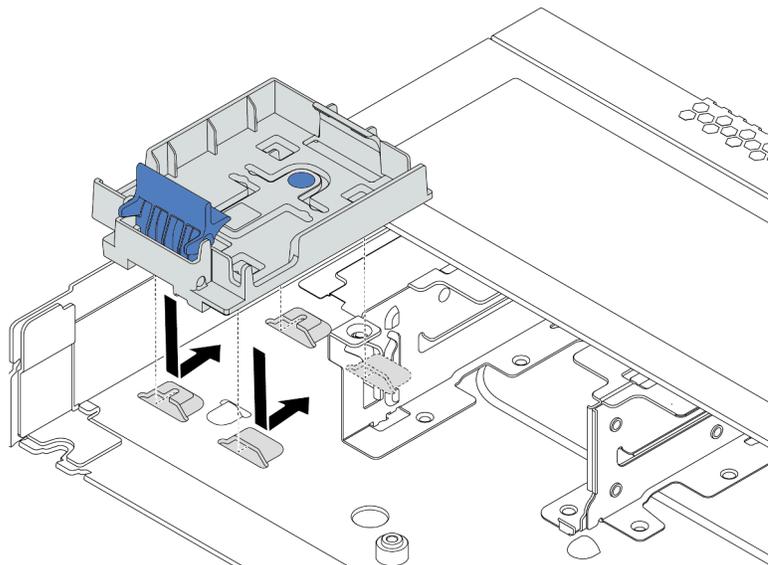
Installazione del supporto del modulo di alimentazione flash RAID
